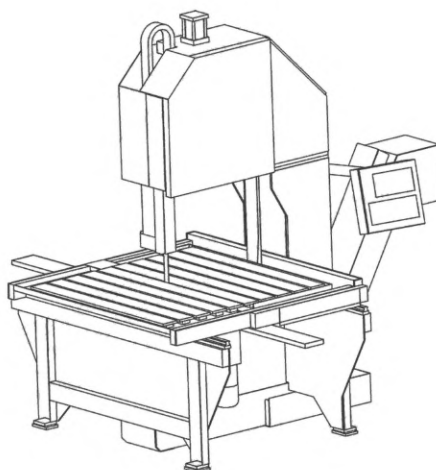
Пильный станок с подачей стола — перемещающийся тип
